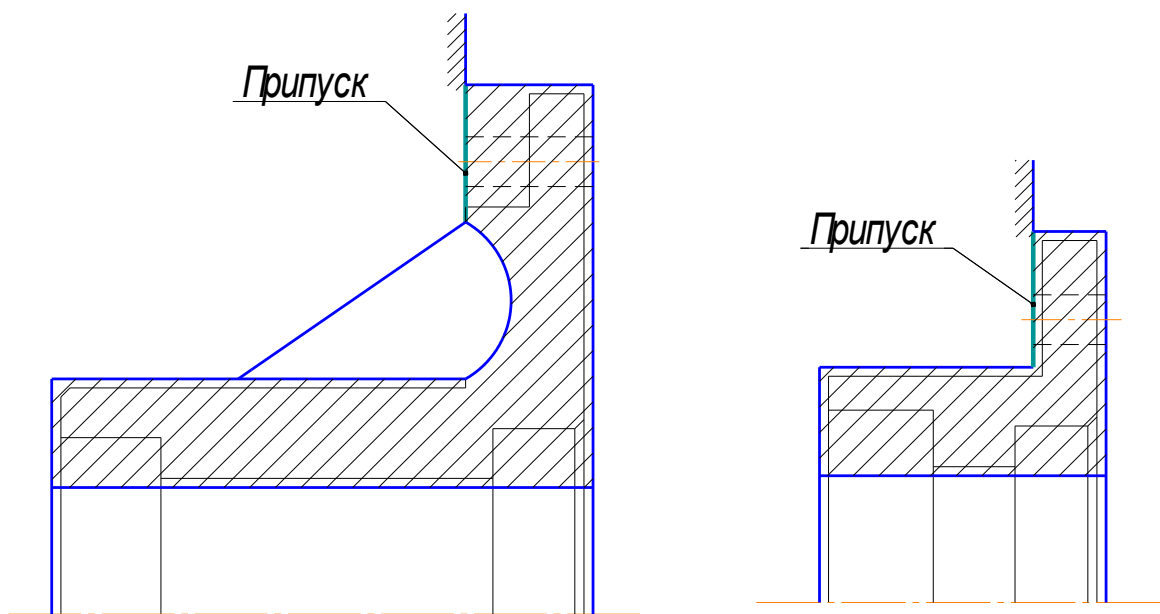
Схема розміщення площини роз'єму відливки для машинної формовки її моделі
